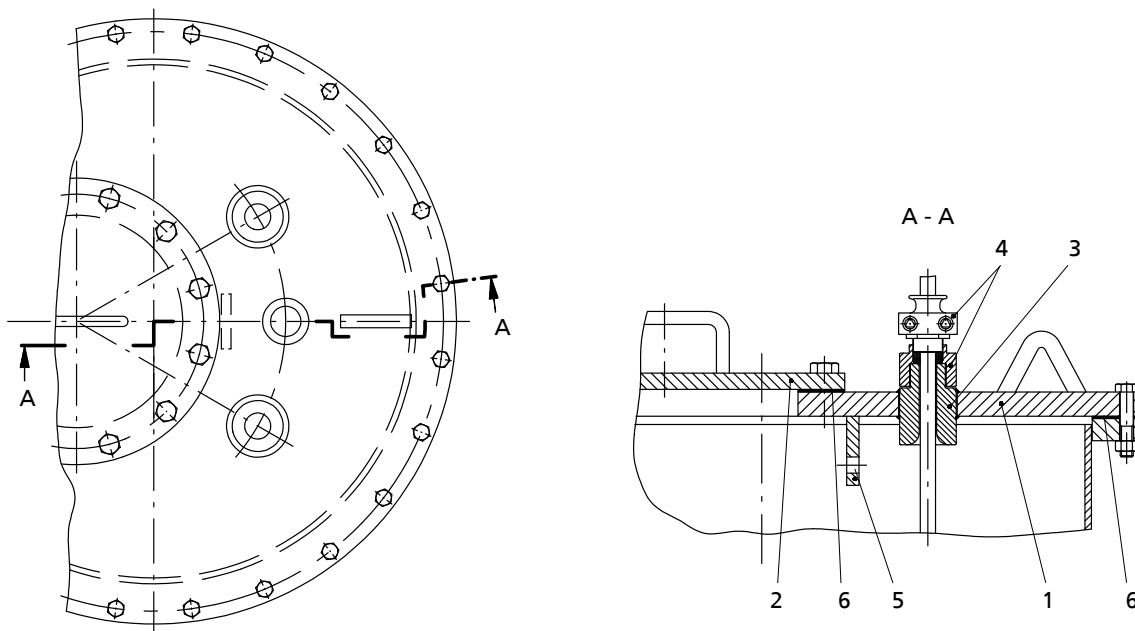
Ausführungsvariante: mit Einschweißhülse
